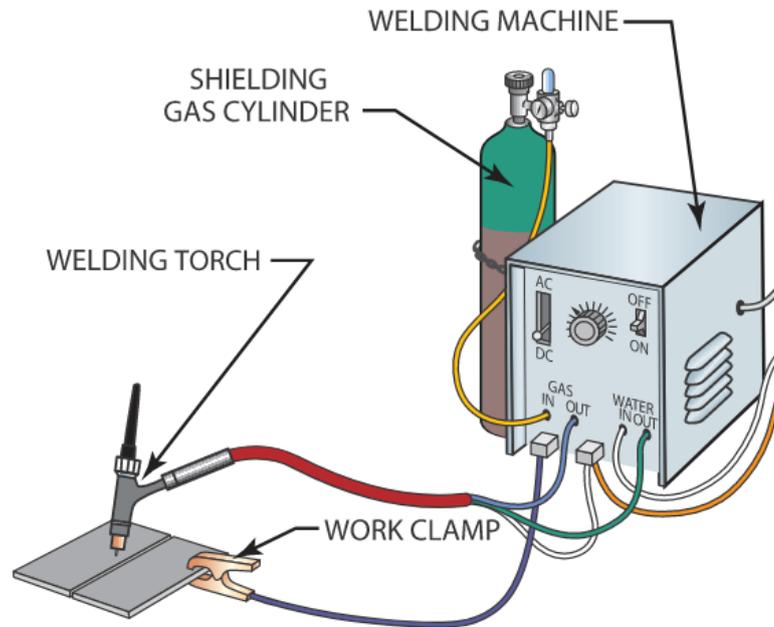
Equipamentos principais da soldadura GTAW (JEFFUS, 2012).
